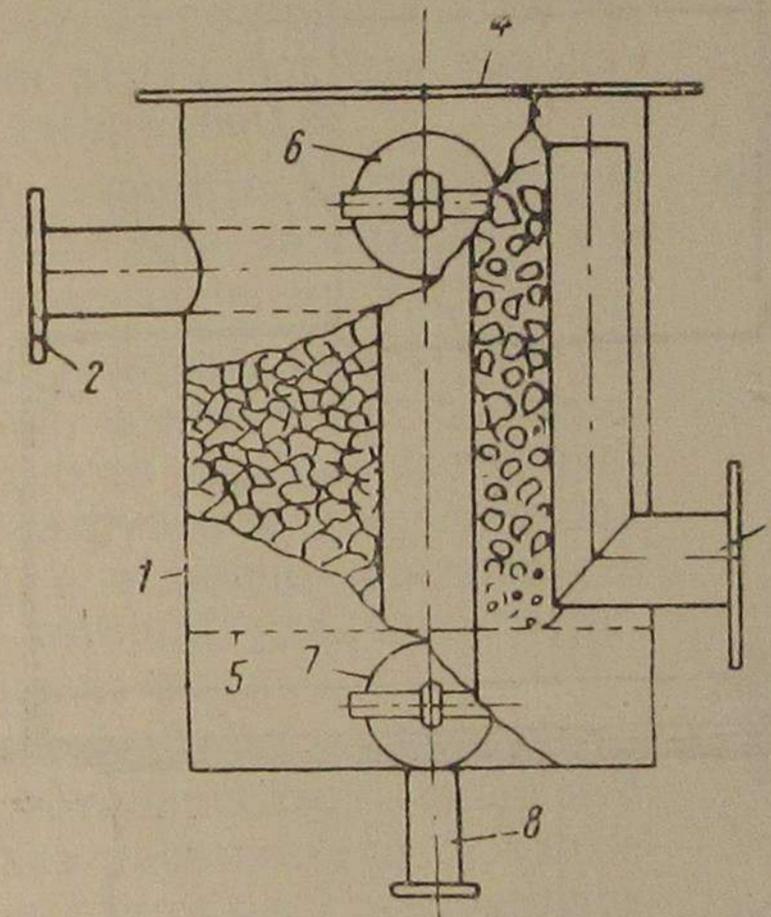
Фильтр тонкой очистки газогенераторной установки для двигателя мощностью 30 л. с.
